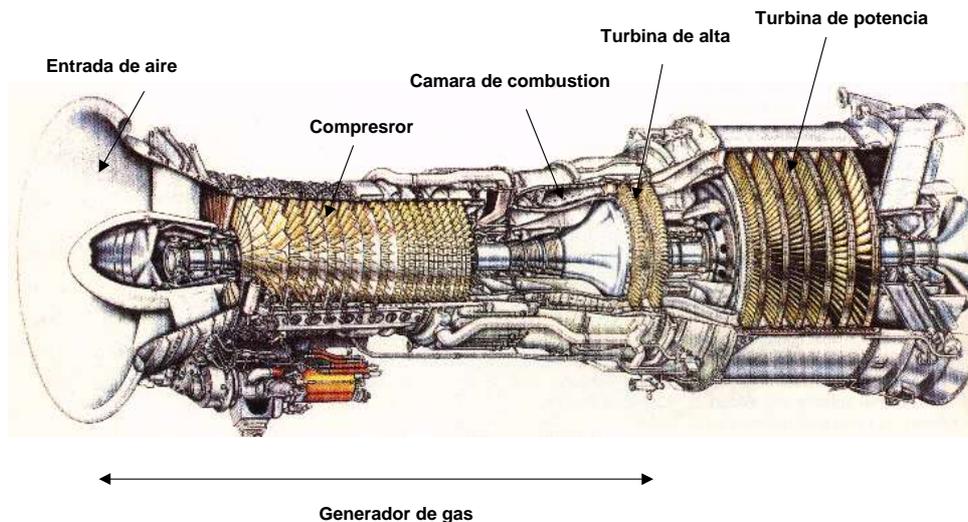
TURBINA DE GAS AERODERIVADA LM 2500
